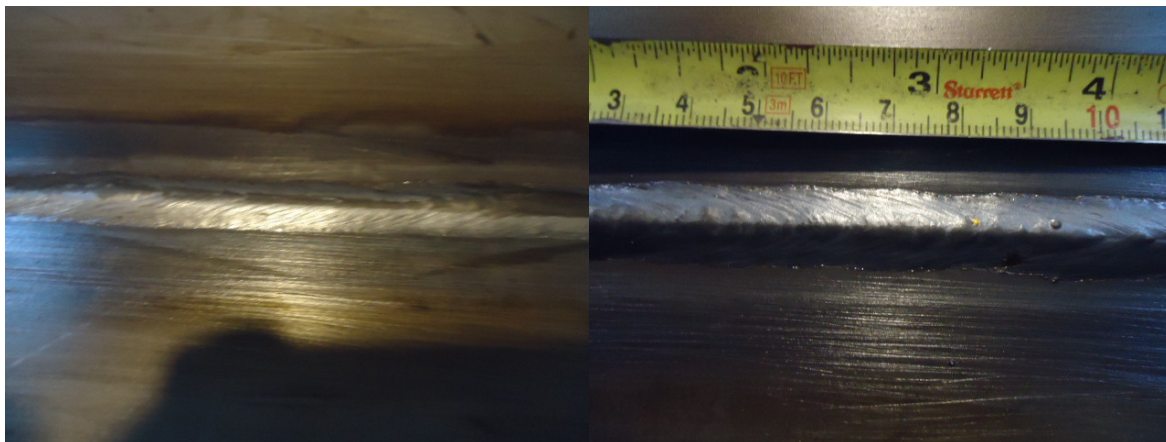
Chapa teste soldada com mistura 20% CO_2
